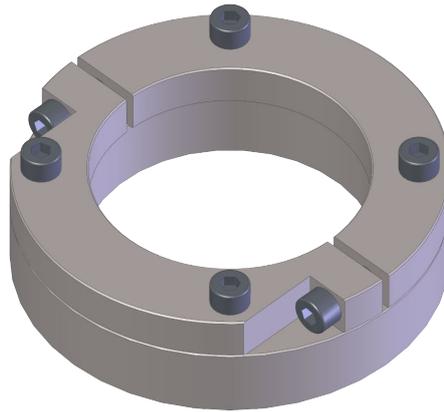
Bague de serrage assemblée et installée sur la plaque de fixation
